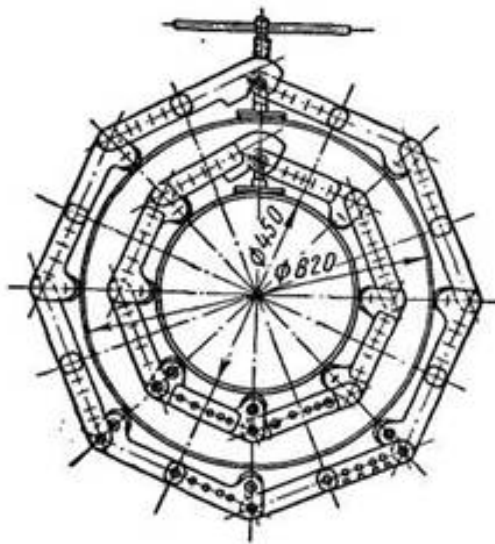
Безмоментний центратор що охоплює універсальної конструкції (в двох положеннях)
